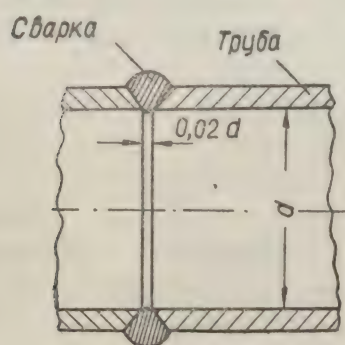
Схема простейшей стыковой сварки труб.
